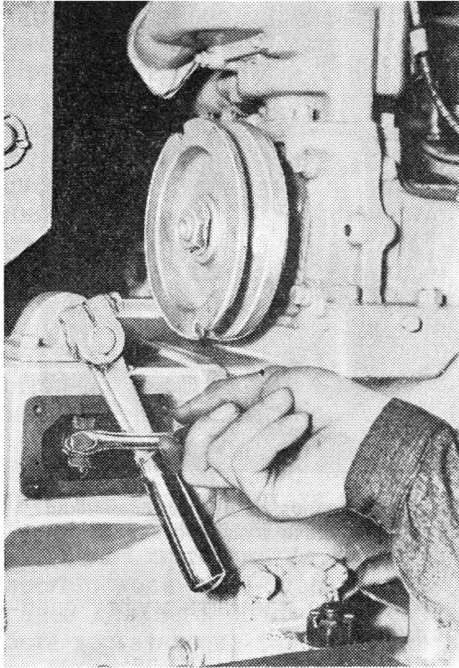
Регулировка механизма автоматического выключения шестерни привода венца маховика при помощи упорного винта
